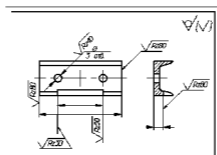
Указание шероховатости, когда большая часть поверхностей не обрабатывается по данному чертежу
